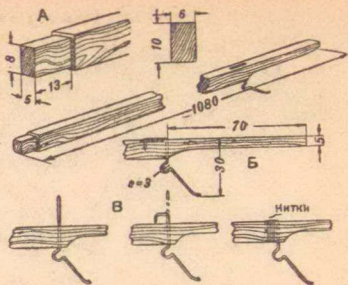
Фюзеляж-рейка: А — передний конец рейки, Б — задний конец рейки и костыль, В — способ и процесс укрепления костыля.
